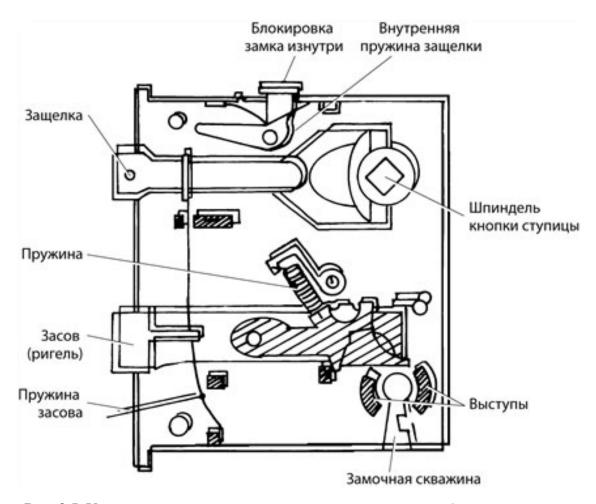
Устройство типичного накладного замка под ключ с бородкой
